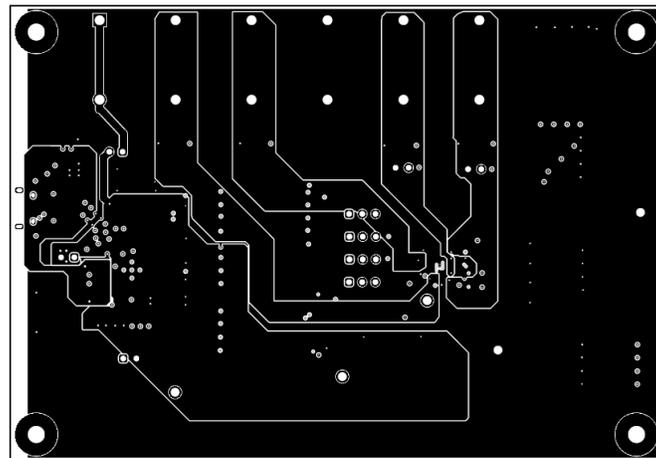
AMC6V704EVM PCB 中层 2 布局 ( 电源层 )
